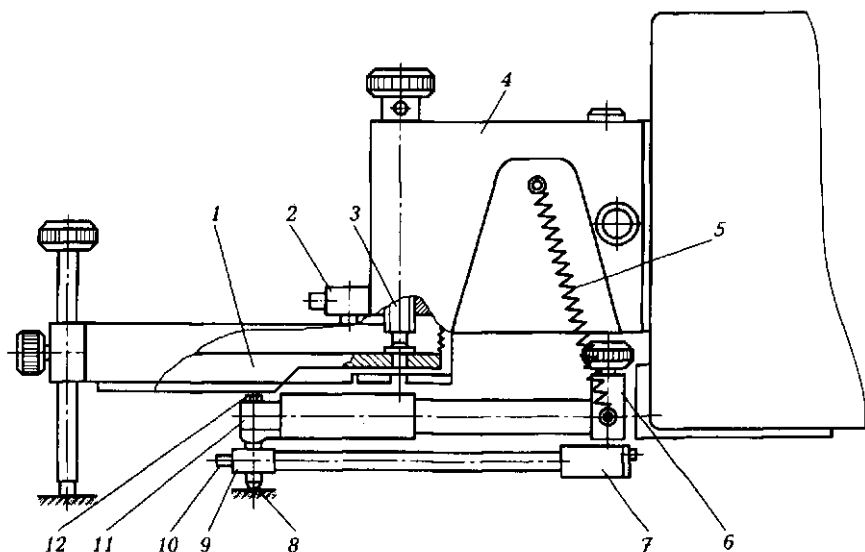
Приспособление для измерения волнистости поверхности:
